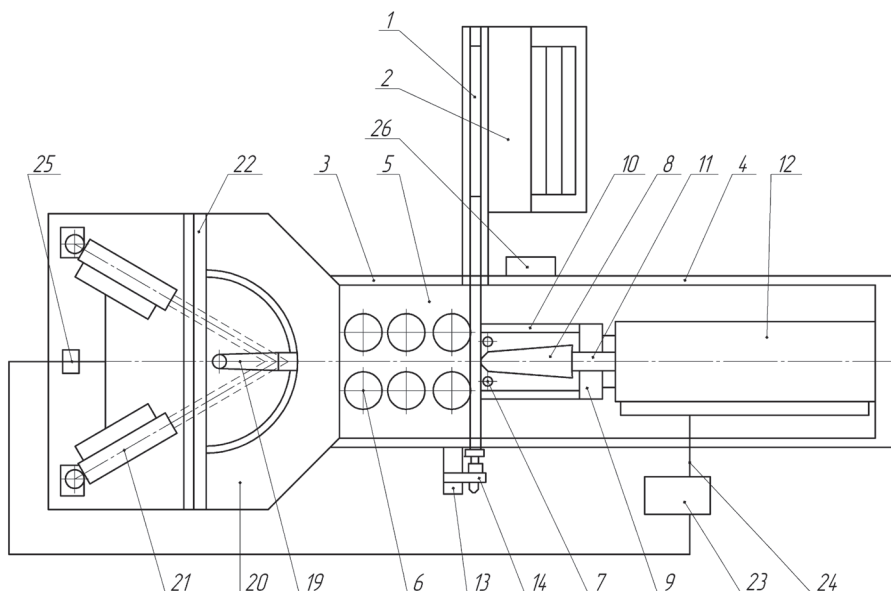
Принципиальная схема стана для прокатки заготовок малолистовых рессор автомобилей МАЗ (вид сверху)
